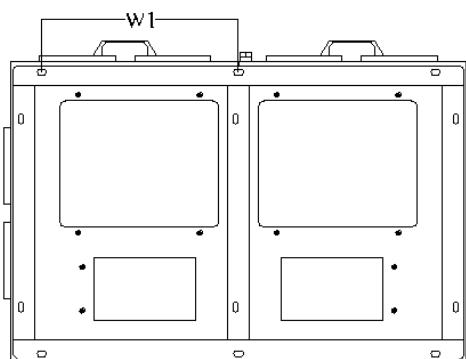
Чертеж преобразователя частоты типоразмер 12
